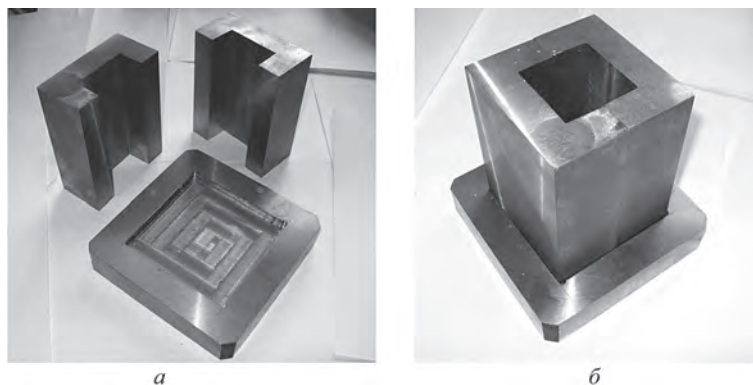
Кокиль для заливки экспериментальных образцов: а – части кокиля; б – кокиль в сборе
